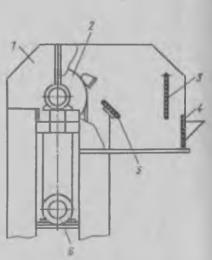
Головка норин У1-УНС-20: 1 — корпус; 2 — барабан; 3 — фартук; 4 — эластичная прокладка; 5 — козырек; 6 — электропривод
